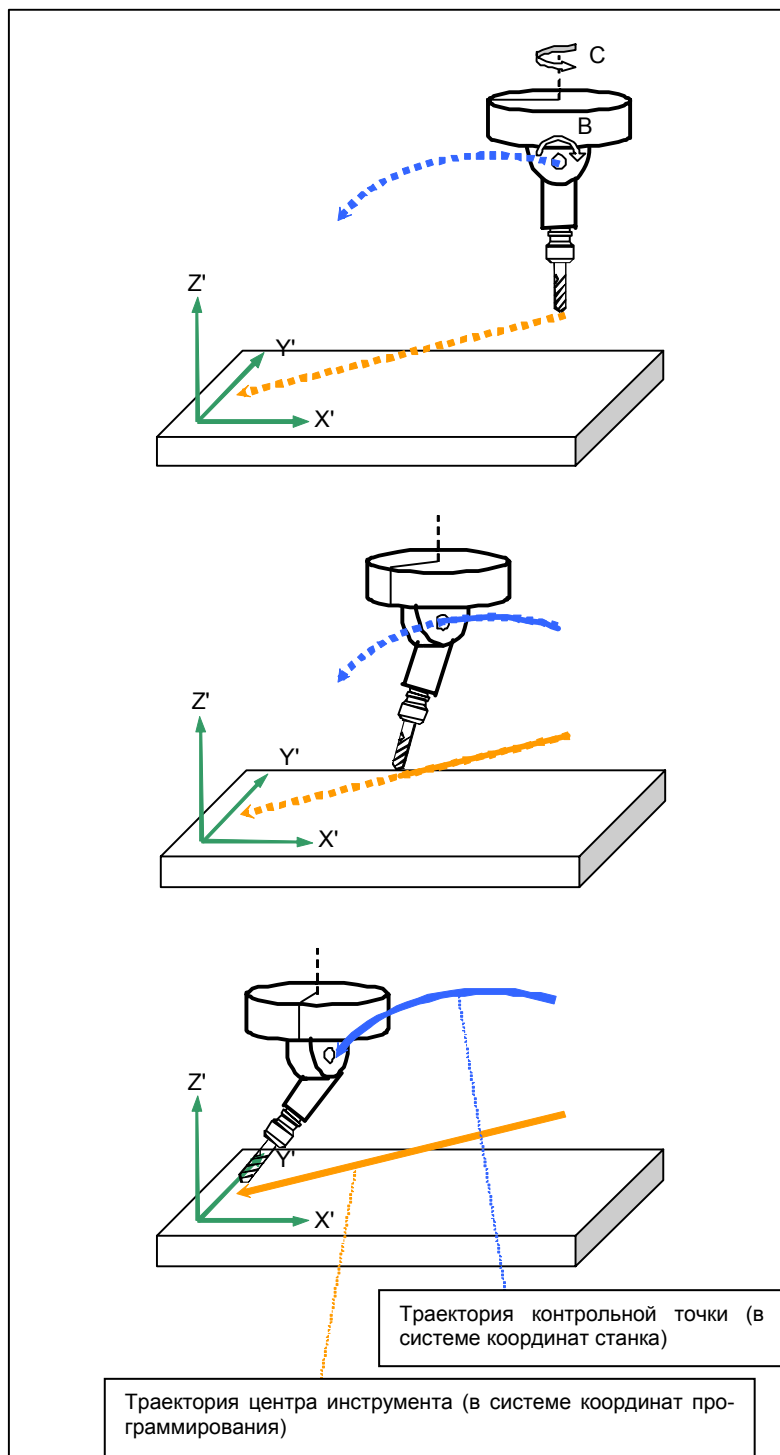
(р) Пример станка с вращающимся инструментом
